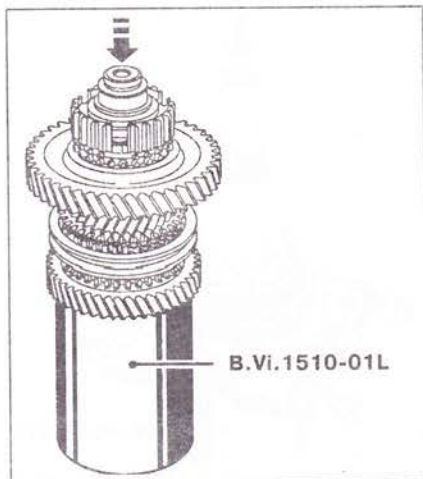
Снимите при помощи пресса сборку «кольцо-шестерня-муфта», подставив под шестерню 3-й передачи приспособление B. Vi. 1510, индекс L.
